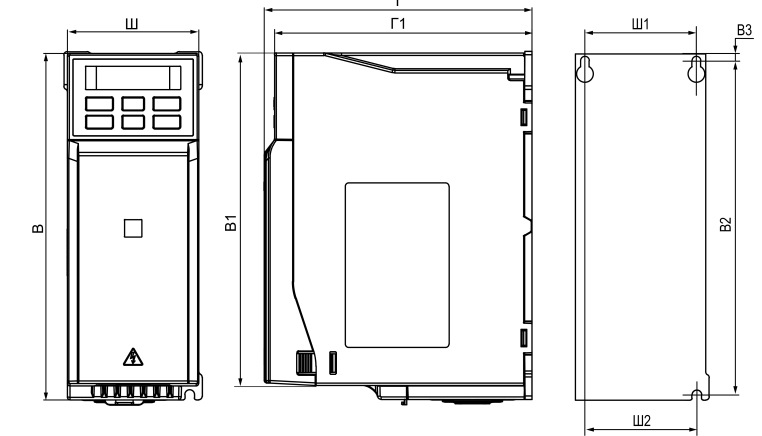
Габаритные размеры прибора в корпусе типоразмера 1
